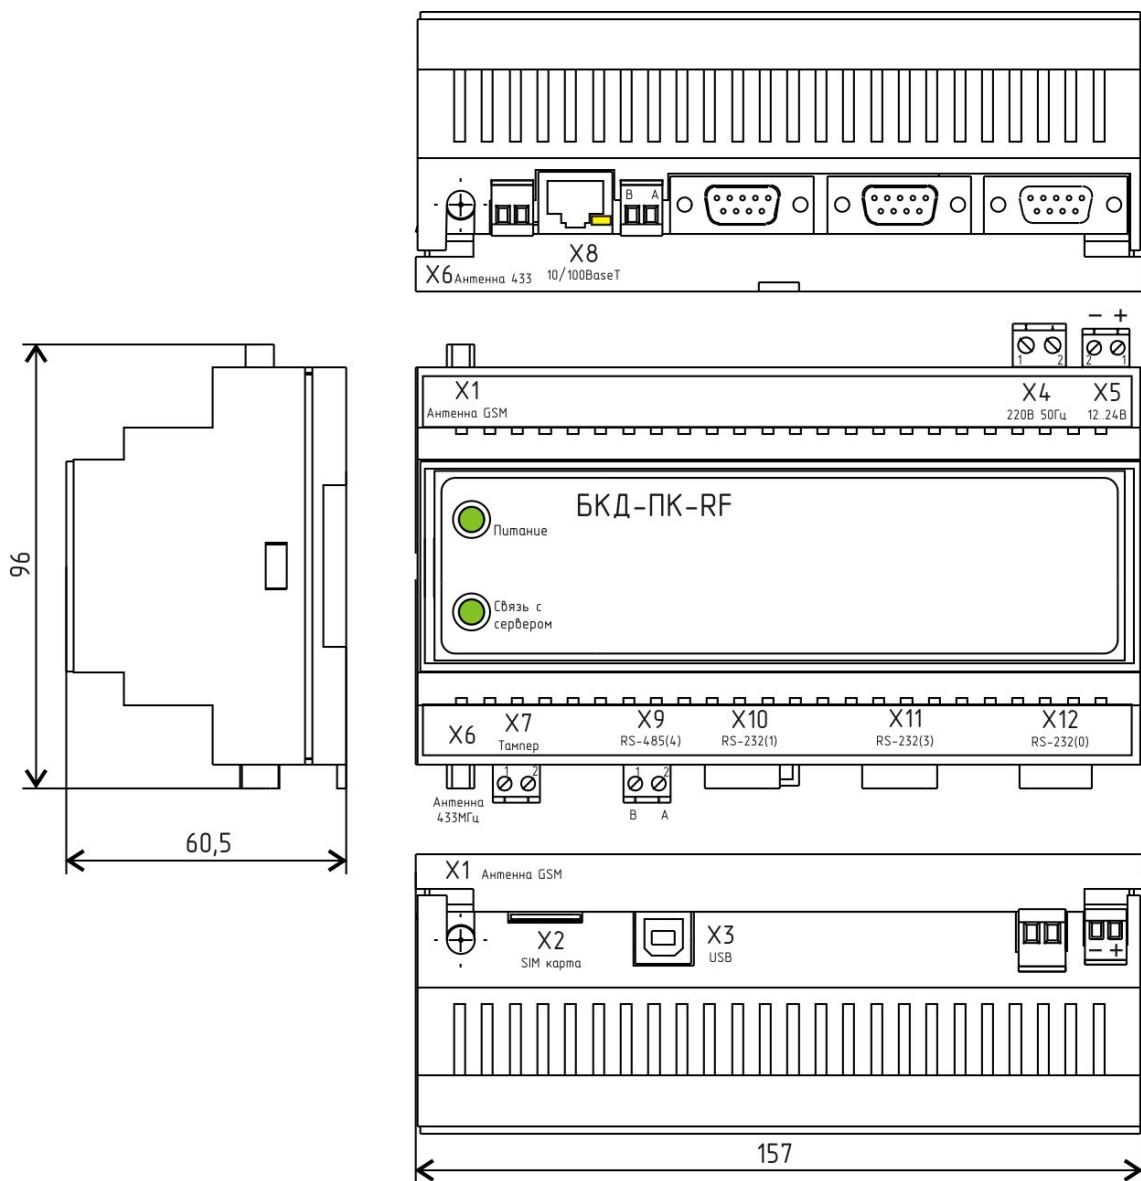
Габаритные размеры БКД-ПК-RF
